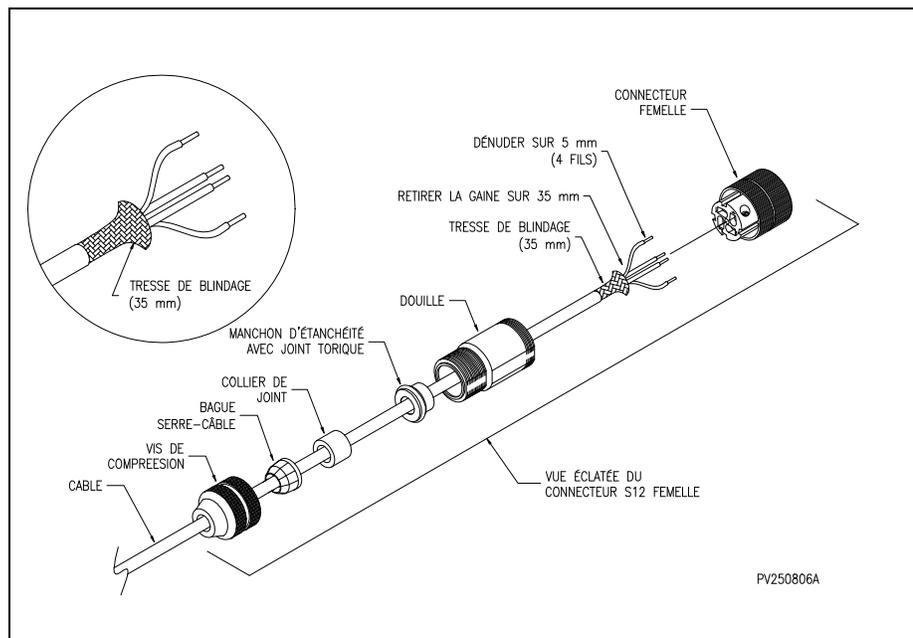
Assemblage en chantier du connecteur M12 femelle au câble d'extension
